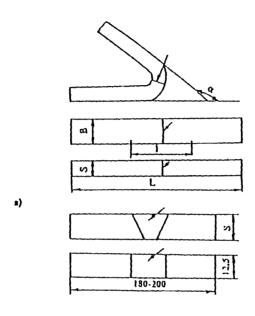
Эскизы образцов (а и б) для механических испытаний сварных соединений на растяжение (размеры даны в габл. 2) по ГОСТ 6996-66: а -тип XII; б - тип XIII
